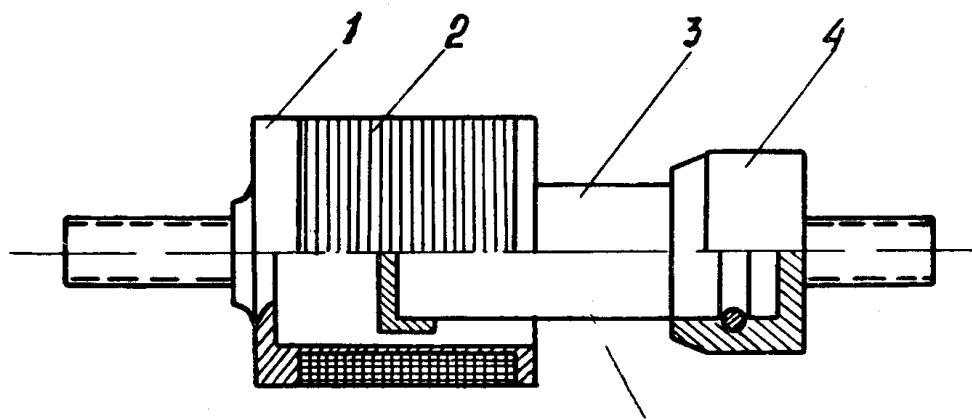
Магнитоэлектрический датчик: 1 — корпус, 2 — обмотка, 3 — магнит, 4 — оправка
